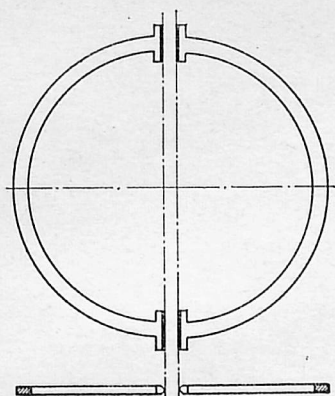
Заготовки для фланца очень большого диаметра.
